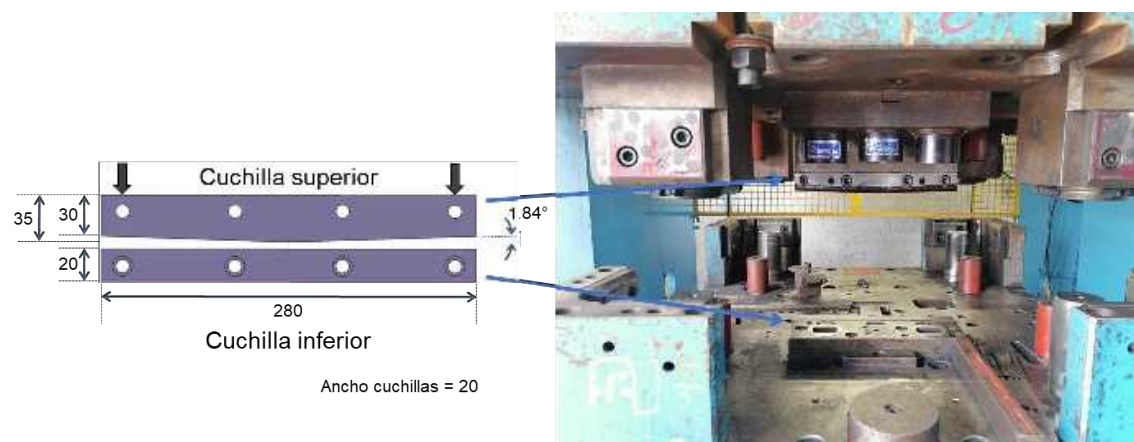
Diseño del herramental para evaluación de corte. Dimensiones en milímetros.
